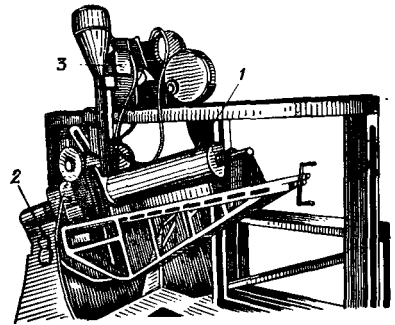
Сварочное приспособление для сварки под флюсом стоек шасси:
